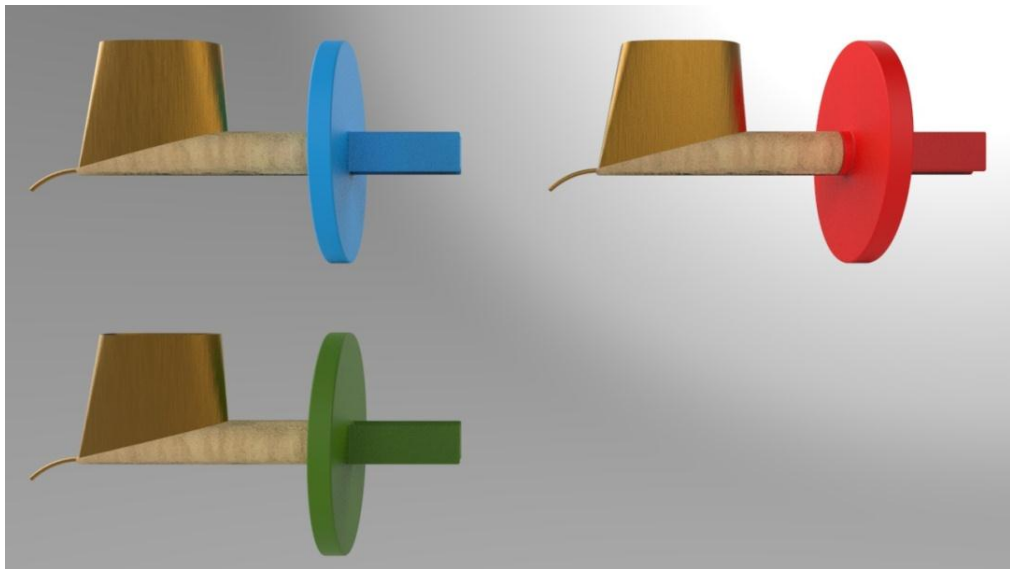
Tampilan tampak depan ke 3 desain usulan canting
